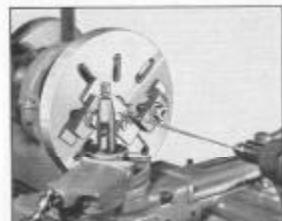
Centrado de la pieza sobre el plato con un indicador de centros
